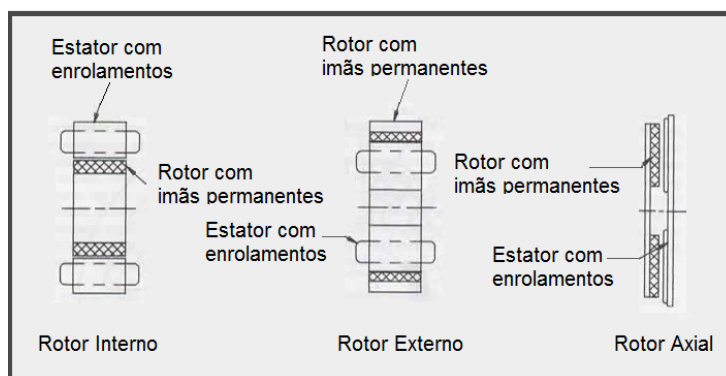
Configurações construtivas rotor interno, rotor externo e rotor axial
